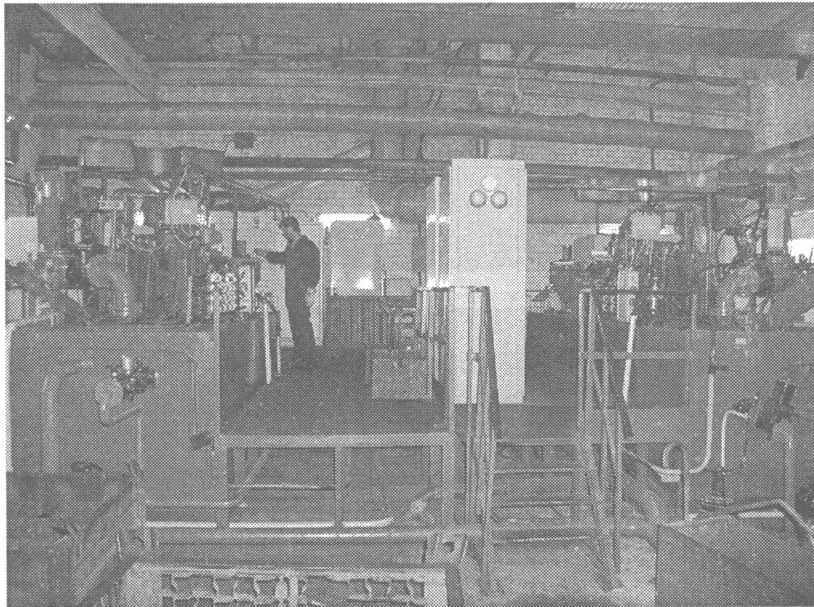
Общий вид участка двух установок для ОПЗ шестерен колесной передачи автомобиля МАЗ
